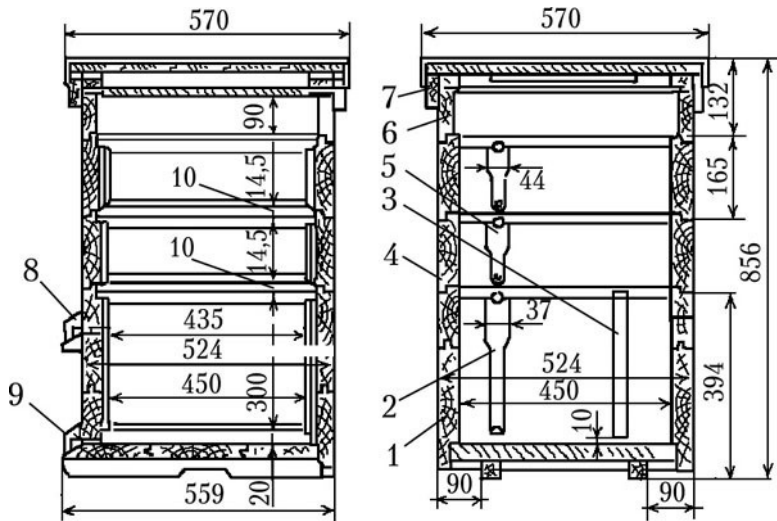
Конструкция двенадцатрамочного улья: 1 – корпус; 2 – рамка гнездовая; 3 – диафрагма; 4 – магазин; 5 – рамка магазинная; 6 – подкрышник; 7 – крыша; 8 – задвижка верхнего летка; 9 – задвижка нижнего летка
